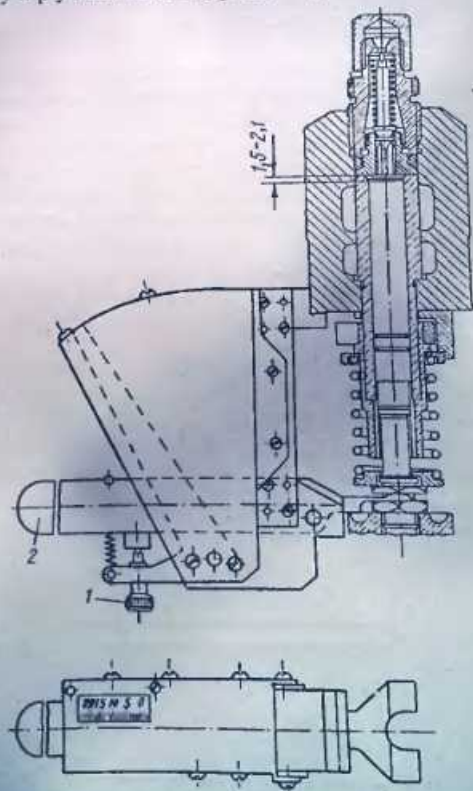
Приспособление JM9579-245 для проверки зазора между верхним торцом плунжера и седлом нагнетательного клапана
